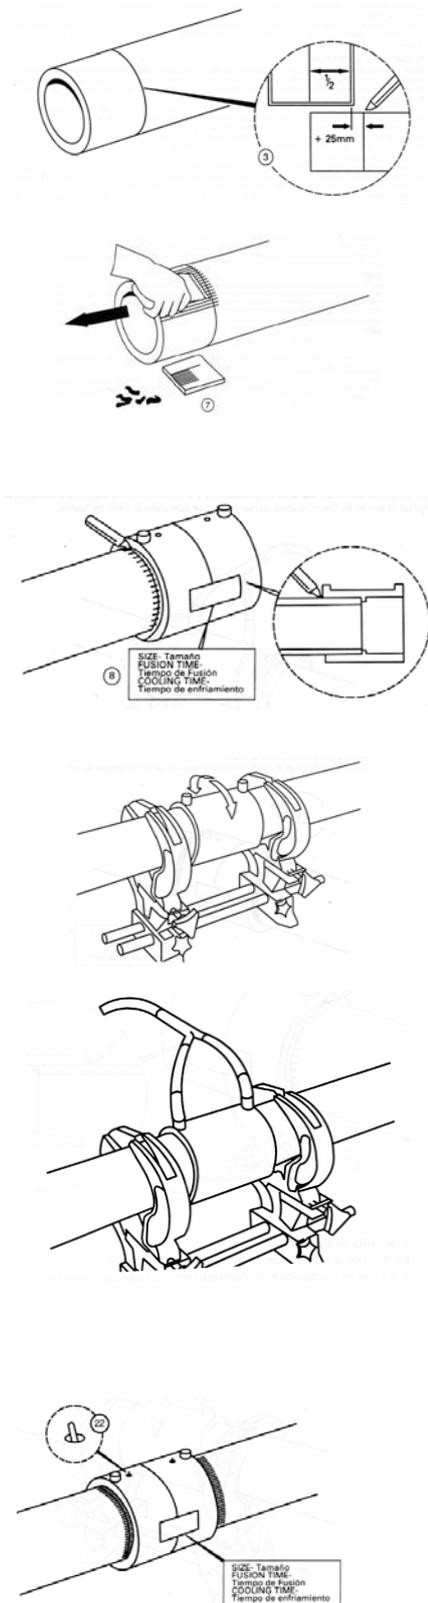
Proceso de soldadura EF con manguitos
